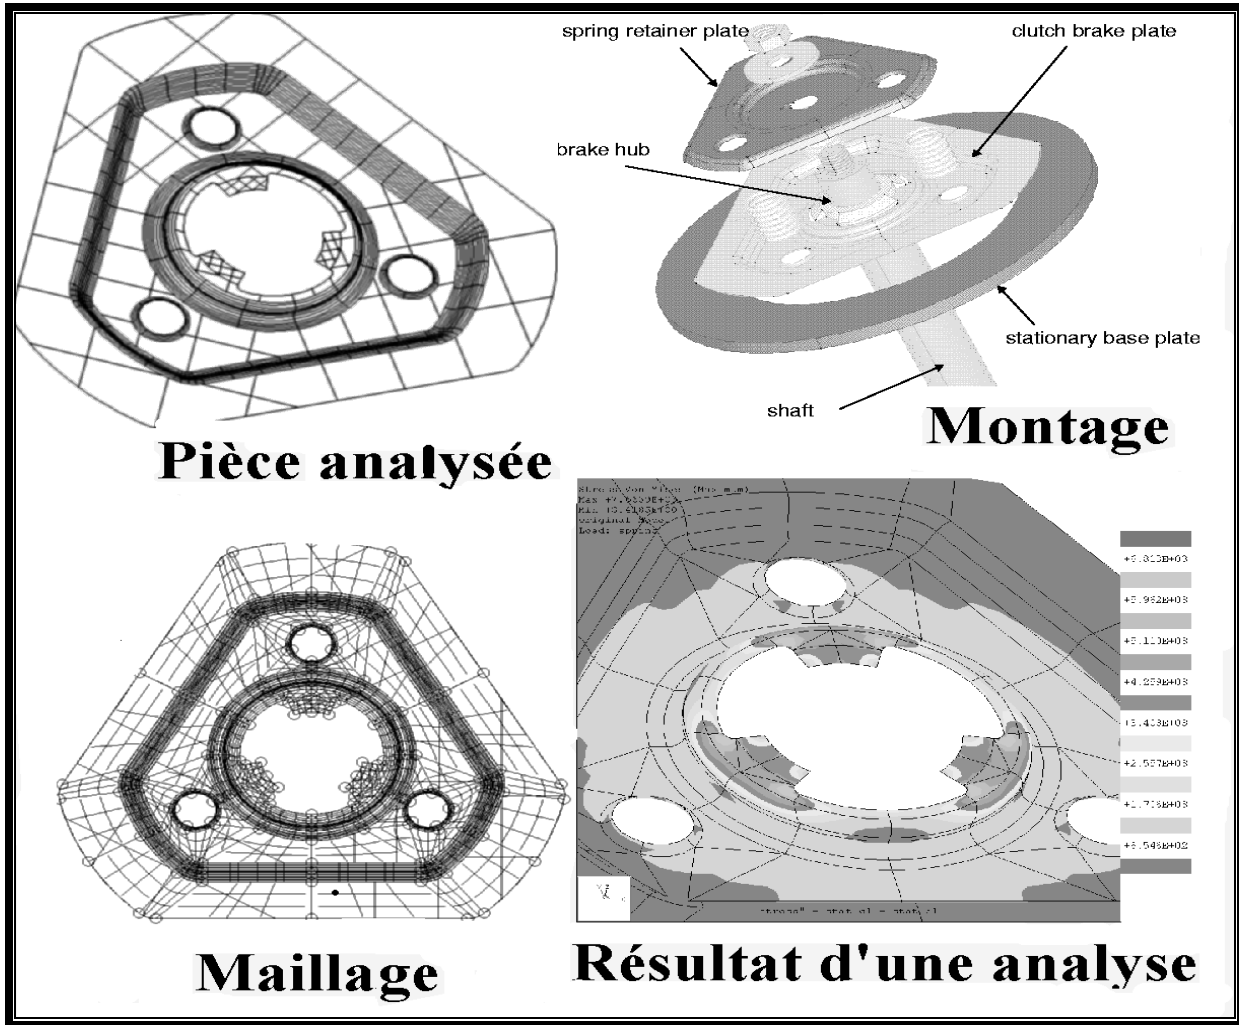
Planches générées avec Pro/ENGINEER et le module Structure de Pro/MECHANICA
